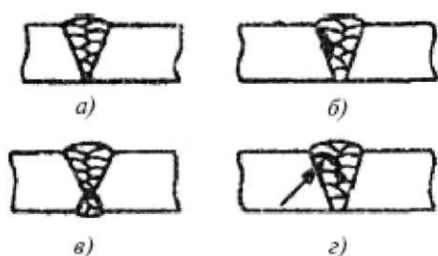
Непровары в сварном шве: а - в корне одностороннего стыкового шва; б - по кромке между основным и наплавленным металлом; в - в корне двустороннего шва; г - между слоями сварного шва
